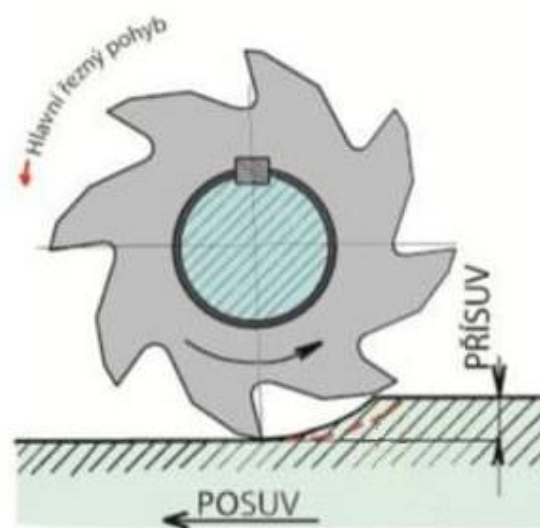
Frézování rovinné plochy válcovou frézou [20].
